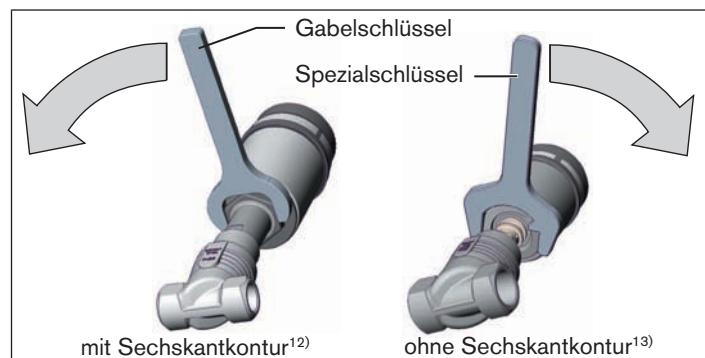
Drehen mit Gabelschlüssel / Spezialschlüssel
